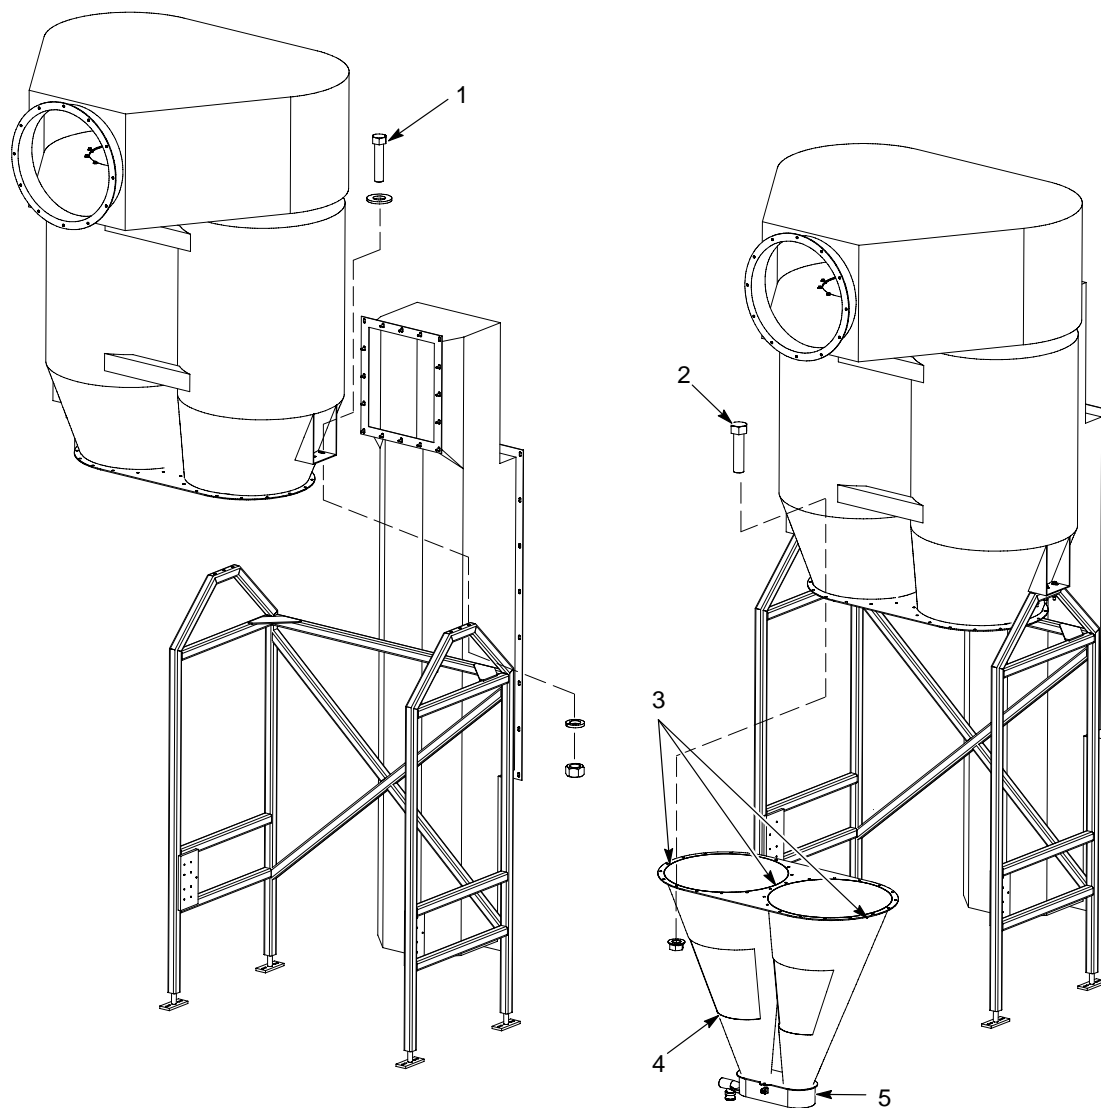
Montagem dos ciclones na estrutura de suporte e completamento do conjunto
